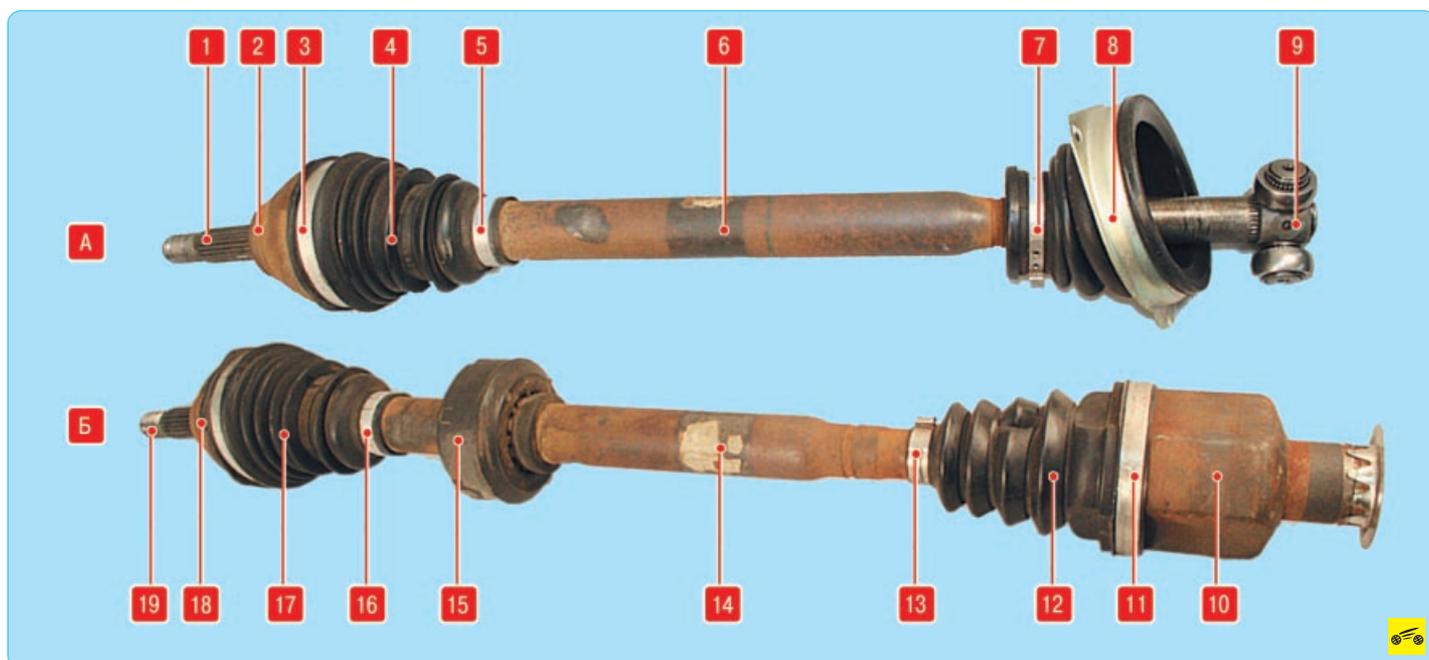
Приводы передних колес: А – привод левого переднего колеса; Б – привод правого переднего колеса; 1 – шлицевый наконечник; 2, 18 – наружные шарниры; 3, 5, 7, 11, 13, 16 – хомуты; 4, 7, 12, 17 – чехлы; 6, 14 – валы привода передних колес; 8 – держатель чехла; 9 – левый внутренний шарнир; 10 – правый внутренний шарнир; 15 – динамический демпфер; 19 – резьбовой наконечник
